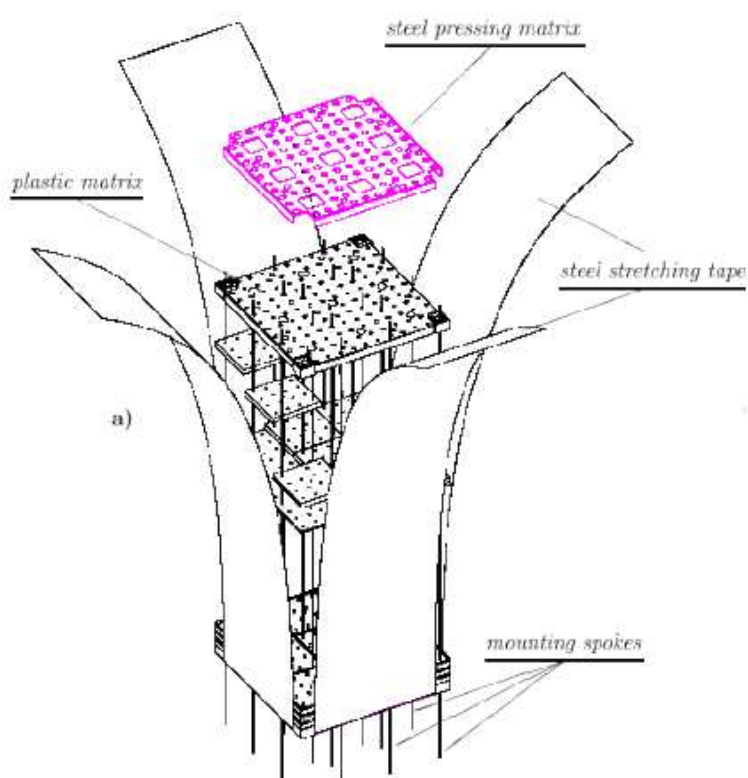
Vue de l'assemblage mécanique d'une tour.
